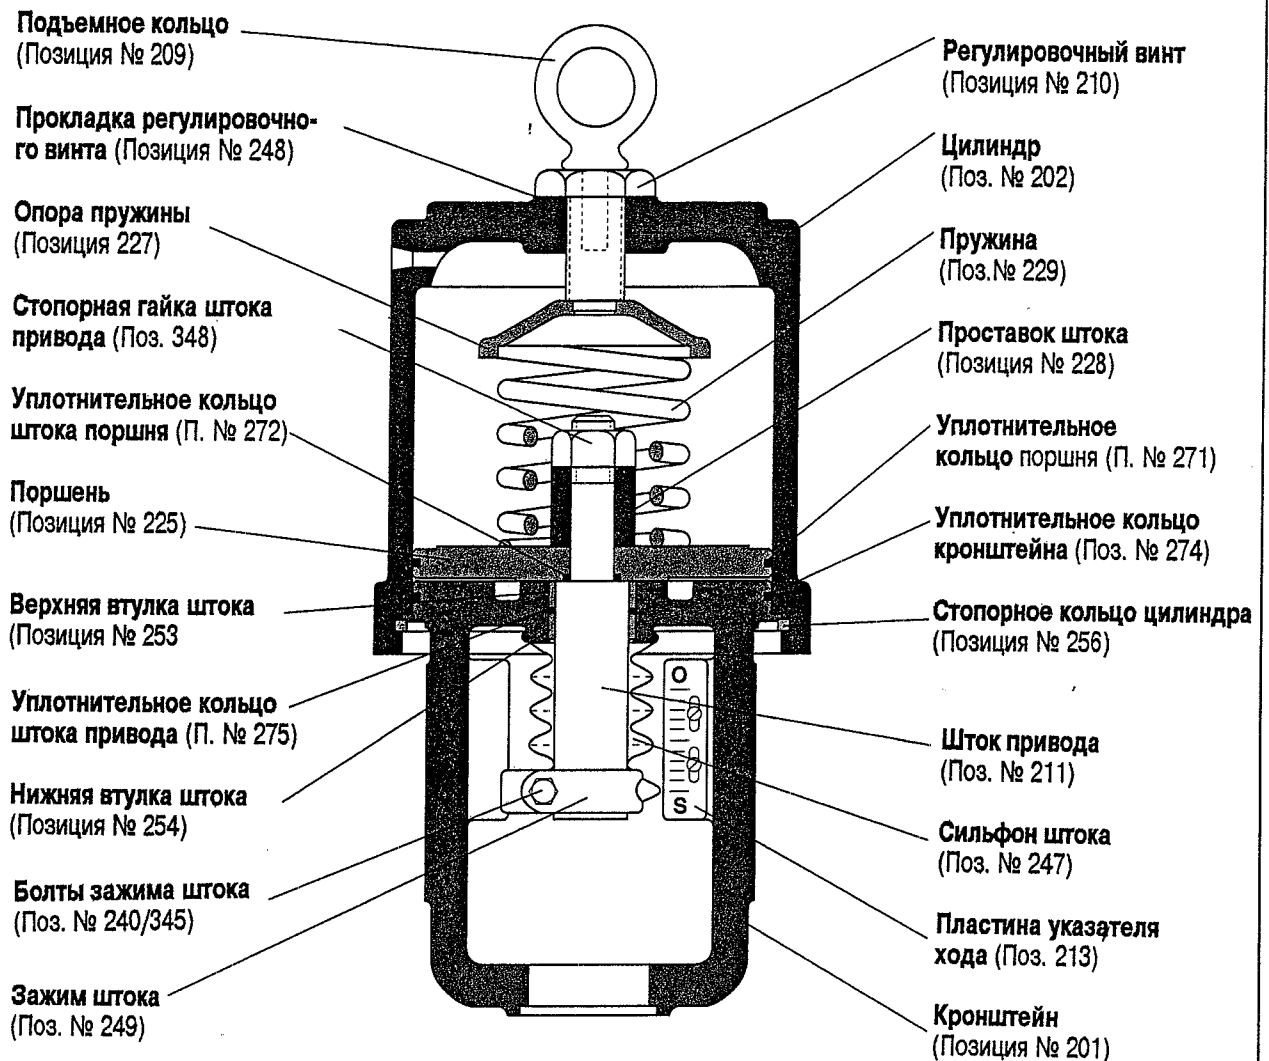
Цилиндр привода с втягивающимся под давлением воздуха штоком
